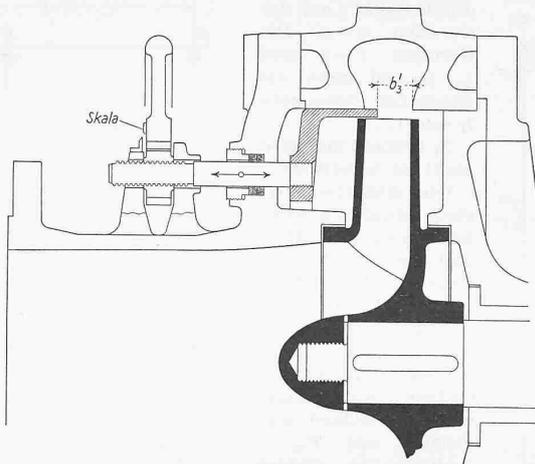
Schnitt durch einstufige Pumpe mit Spaltschieber
